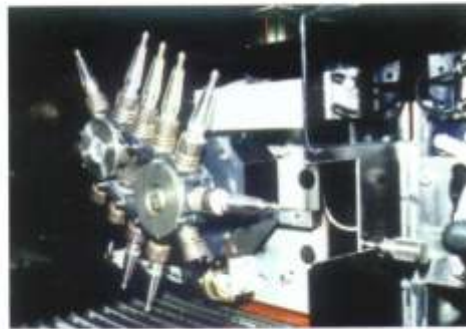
und 20b Das Werkzeugmagazin, aus dem nach Fräsauftrag die Maschine automatisch bestückt wird.
